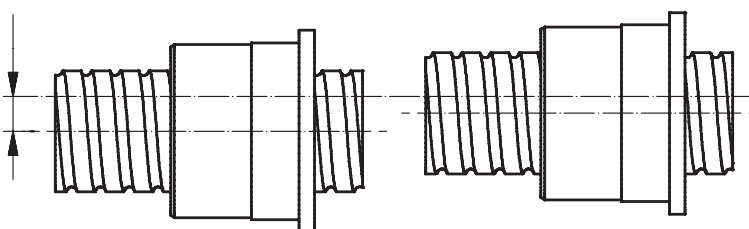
Ausrichten einer Kugelgewindetriebs-Spindel
